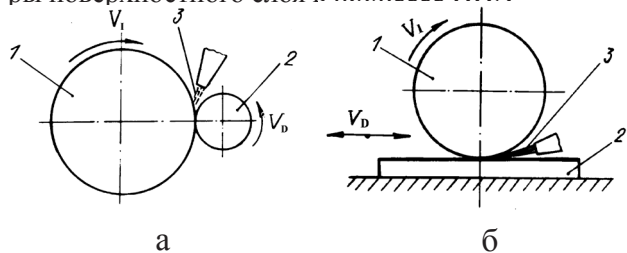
Схема МИО цилиндрических (а) и плоских (б) поверхностей: 1 – упрочняющий инструмент; 2 – обрабатываемая деталь; 3 – технологическая среда (ТС)
